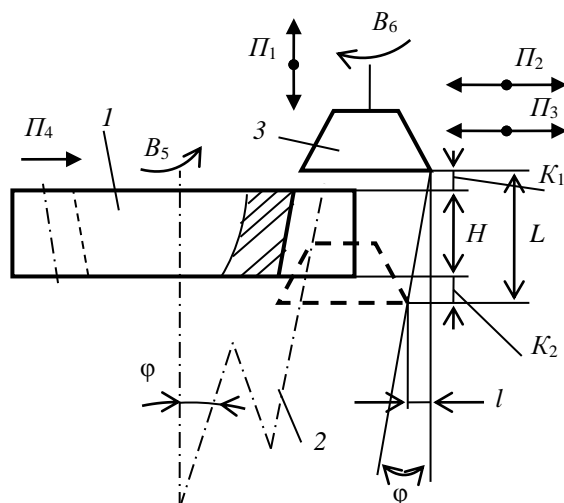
Способ долбления цилиндрических колес с наклонными зубьями
